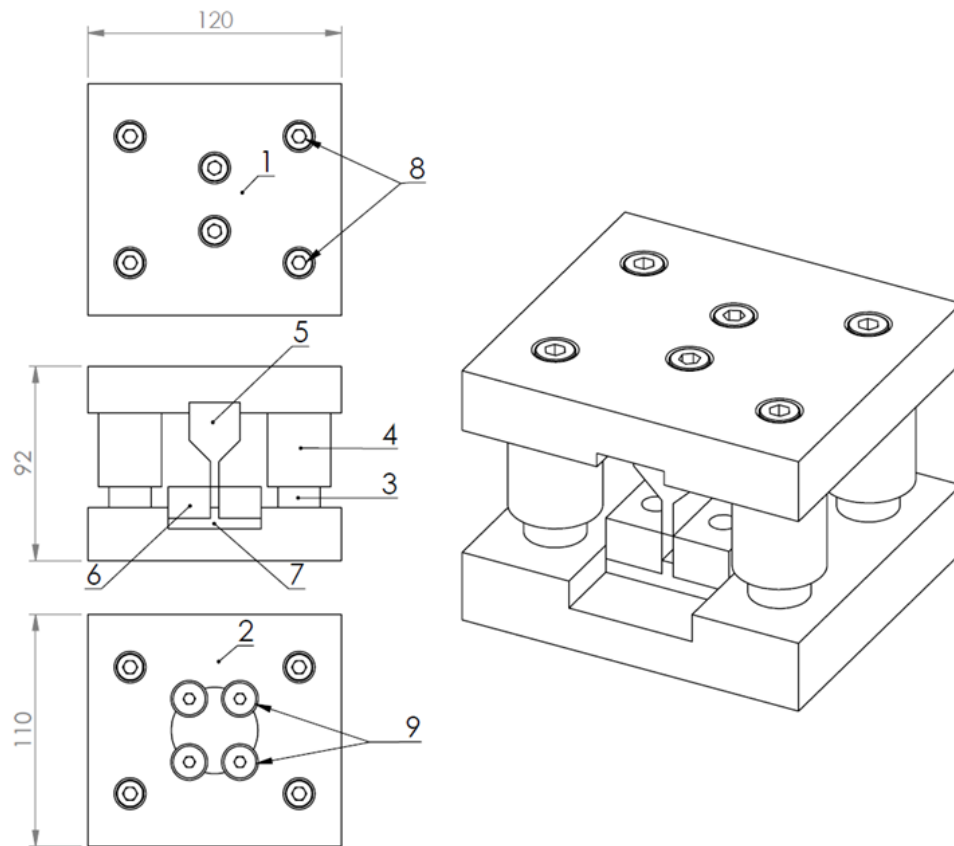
Dibujo de conjunto del dispositivo de compresión plana. 1 Placa superior, 2 placa inferior, 3 barra deslizante, 4 cilindro deslizante, 5 indente, 6 soporte lateral de espécimen, 7 base de espécimen, 8 tornillo M8x1.25, 9 Tornillo cabeza cónica M8x1.25.
